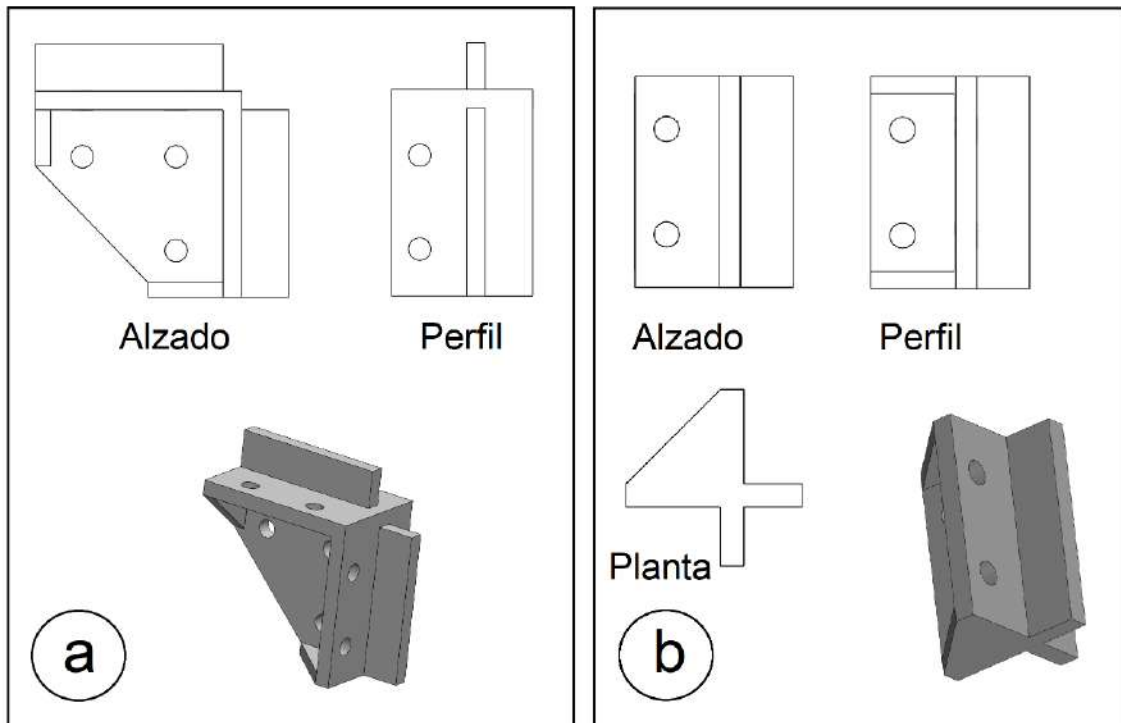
a) Planos y vista 3D de las bridas en escuadra. b) Planos y vista 3D de las bridas rectas.
